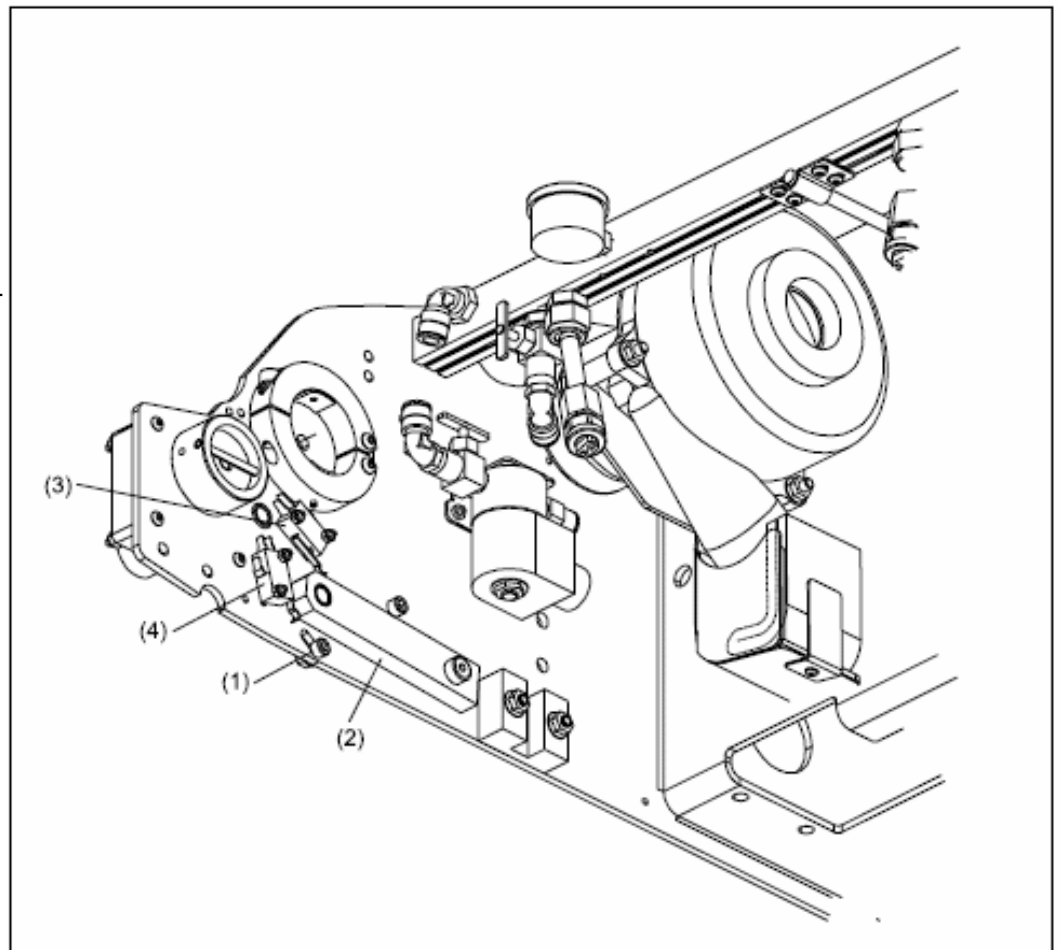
Ajustement arrêt inférieur - Vue de dessous
